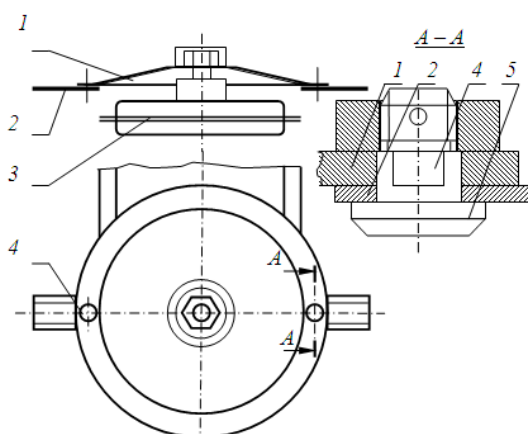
Схема ротора с шарнирно закрепленными на диске ножами
